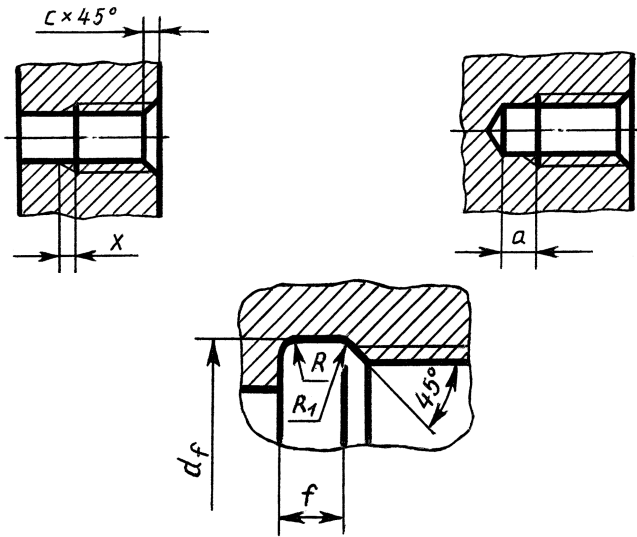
Розміри збігів, недорізів, проточок і фасок для внутрішньої трубної циліндричної різьби
